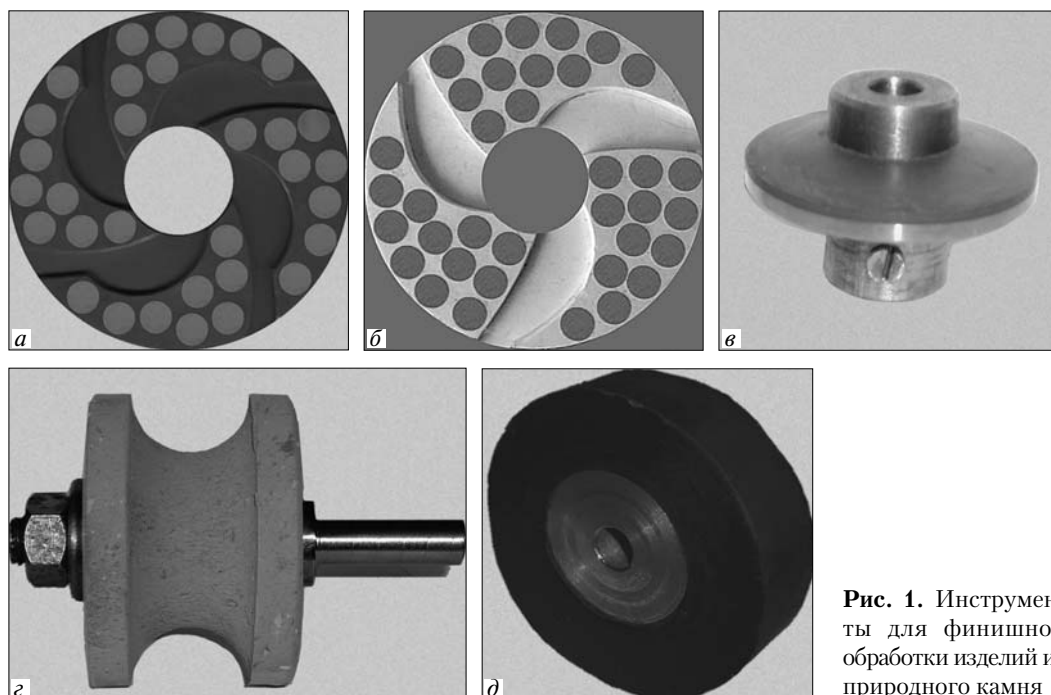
Инструменты для финишной обработки изделий из природного камня
